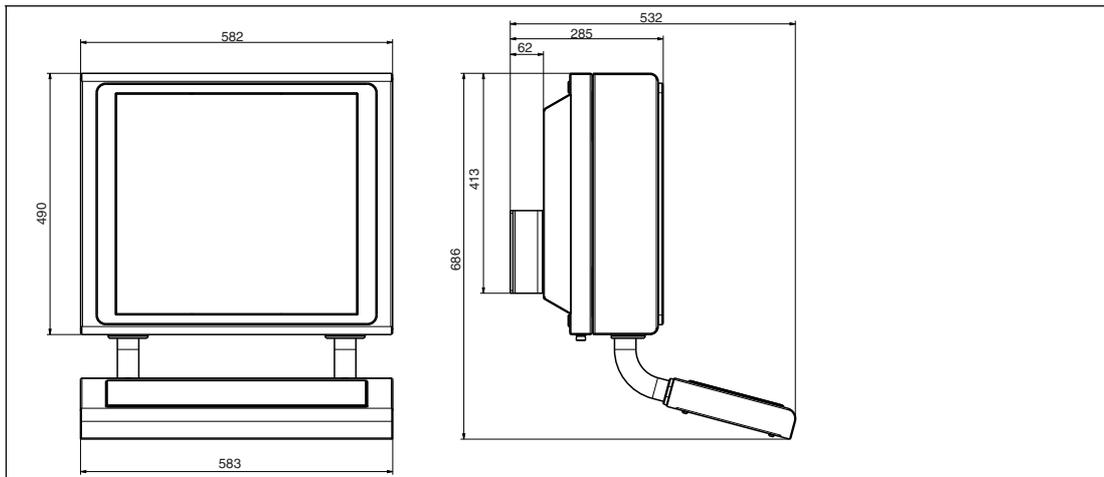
Abmessungen zur Wandmontage mit zusätzlichen Wandhalterungen (Nr. 198768)
